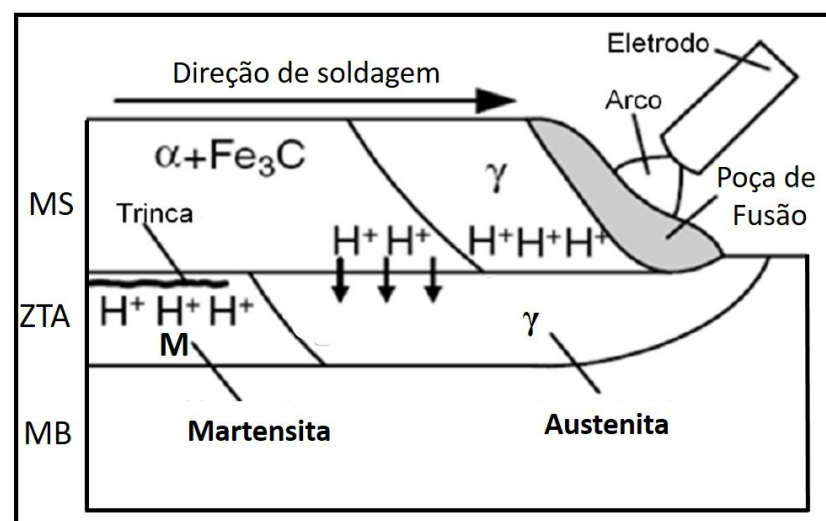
Difusão do hidrogênio do metal de solda para a ZTA durante a soldagem.
